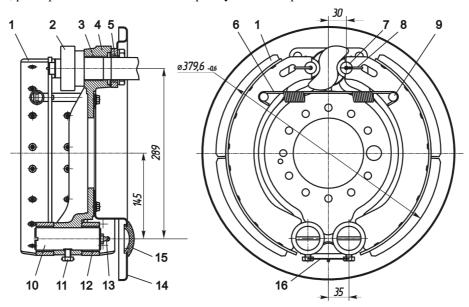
Тормозной механизм автобуса ПАЗ-4234 ("КААЗ")
